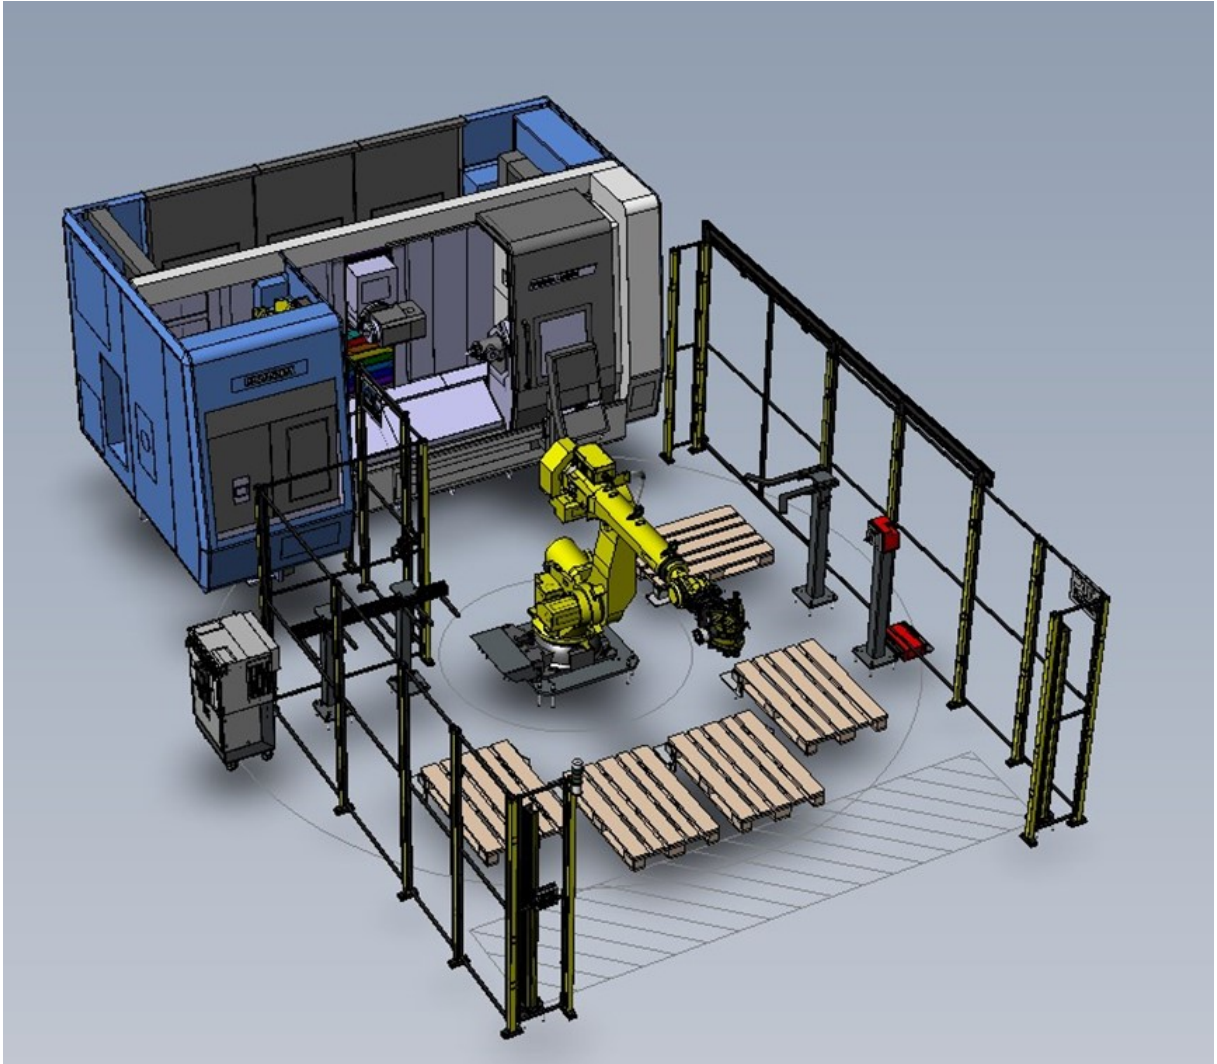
Doosan SMX 3100-sorvi (Doosan Machine Tools n.d-b)
